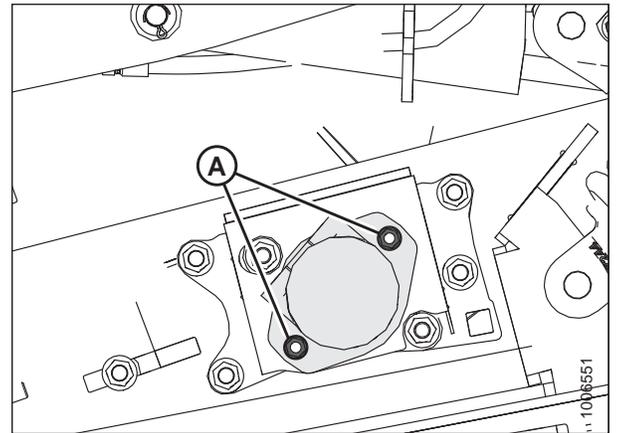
Motor hidráulico delantero; lado izquierdo
